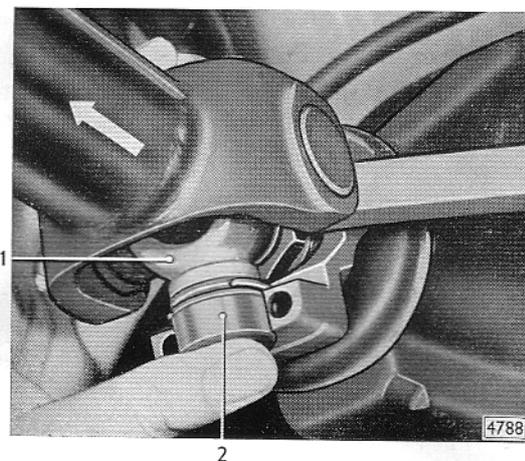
Gelenkwelle vom Antriebskegelradflansch abdrücken
